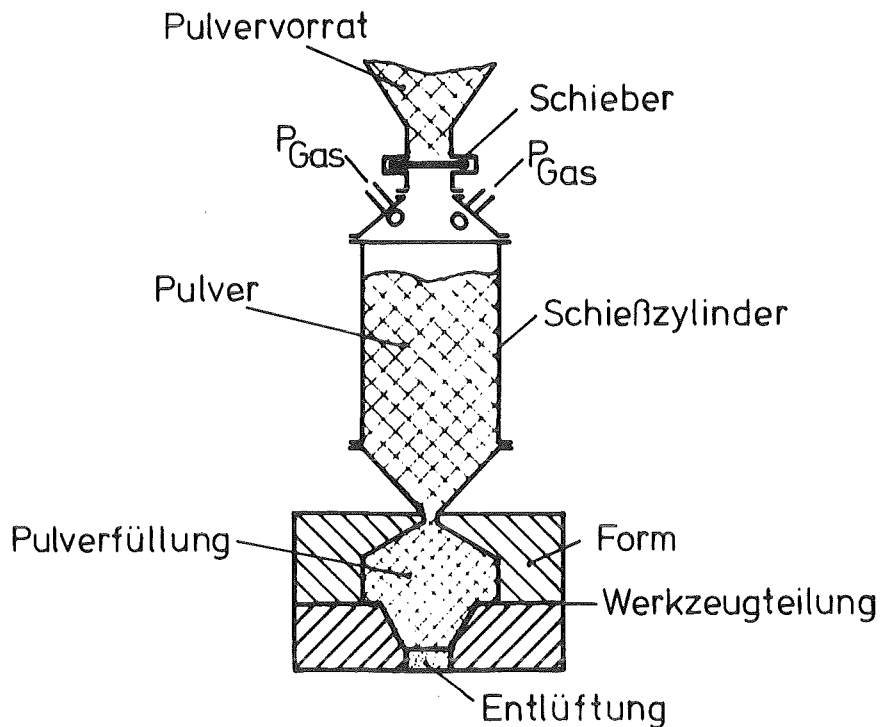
Prinzipieller Aufbau einer Kernschießmaschine
